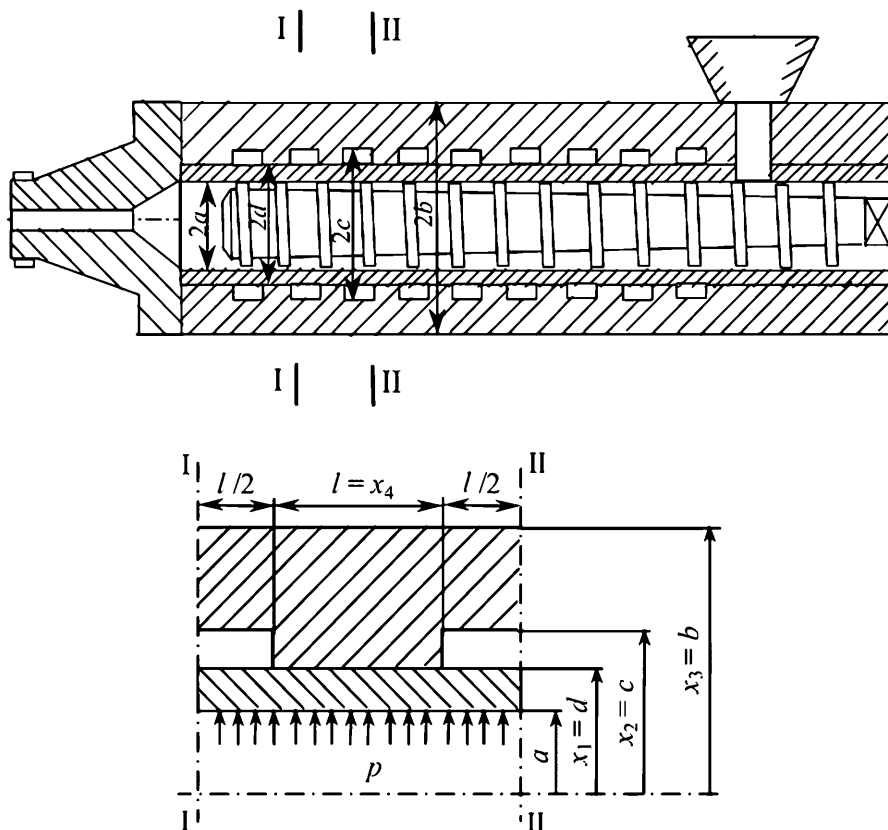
Конструкция двухслойного цилиндра пластикации
